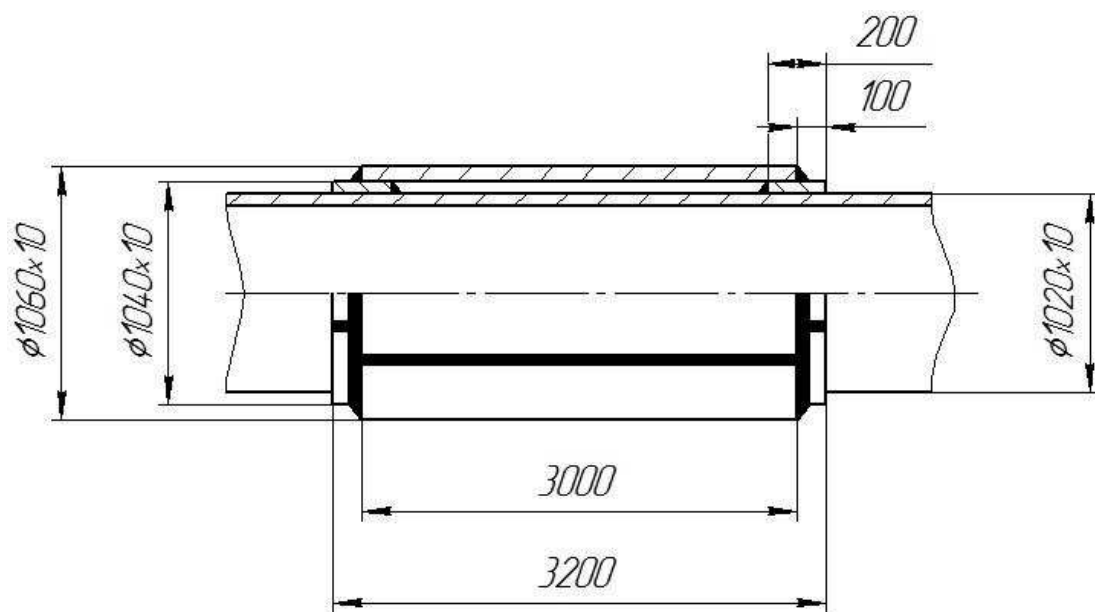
Муфта конструкции №3 для ремонта газопровода Ø1020 мм.
